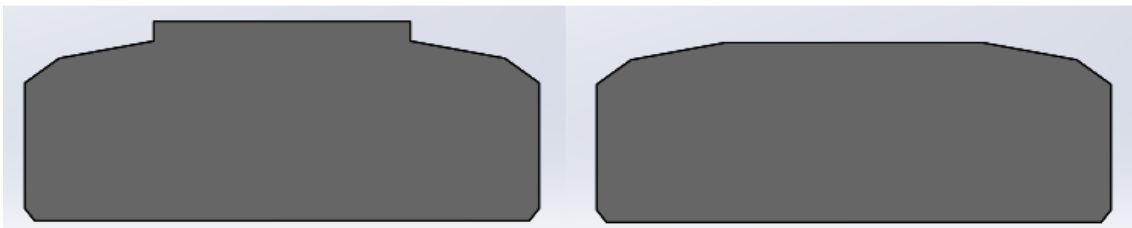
Geometría de las vigas de arriostramiento, SolidWorks.
